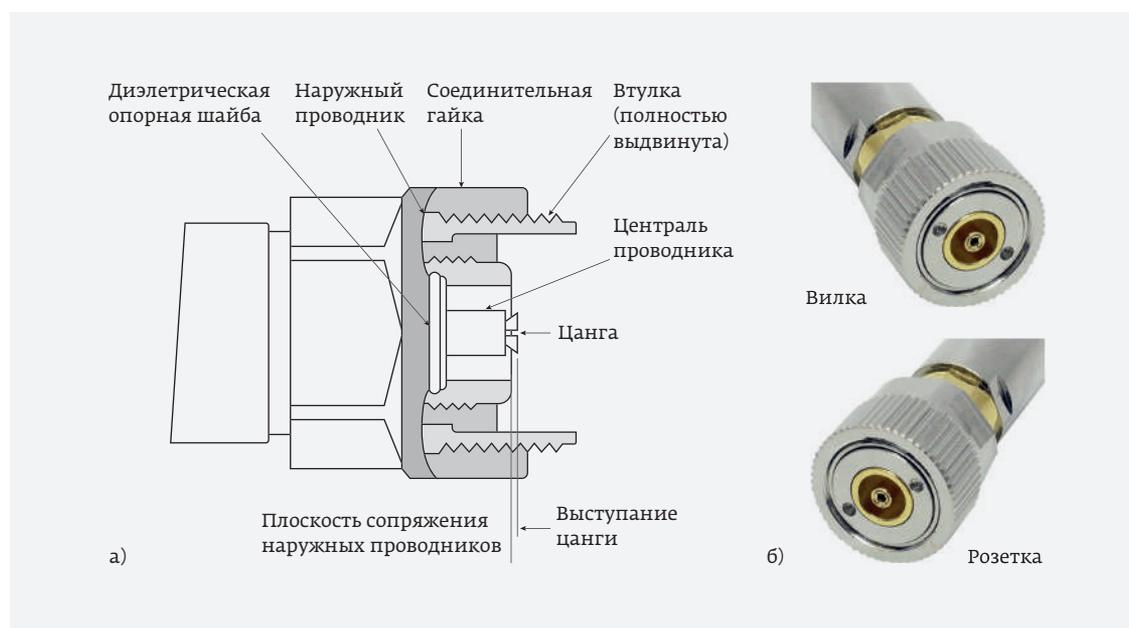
Конструкция (а), внешний вид вилки и розетки соединителя 7 mm (GPC 7) (б)
